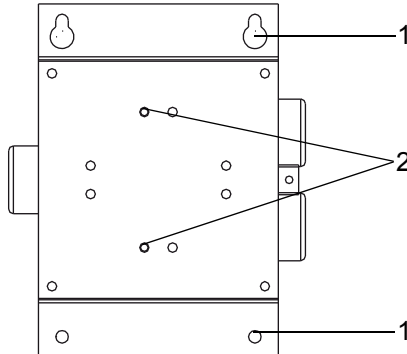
Montageplaat voor ULTIMA XE en XIR
